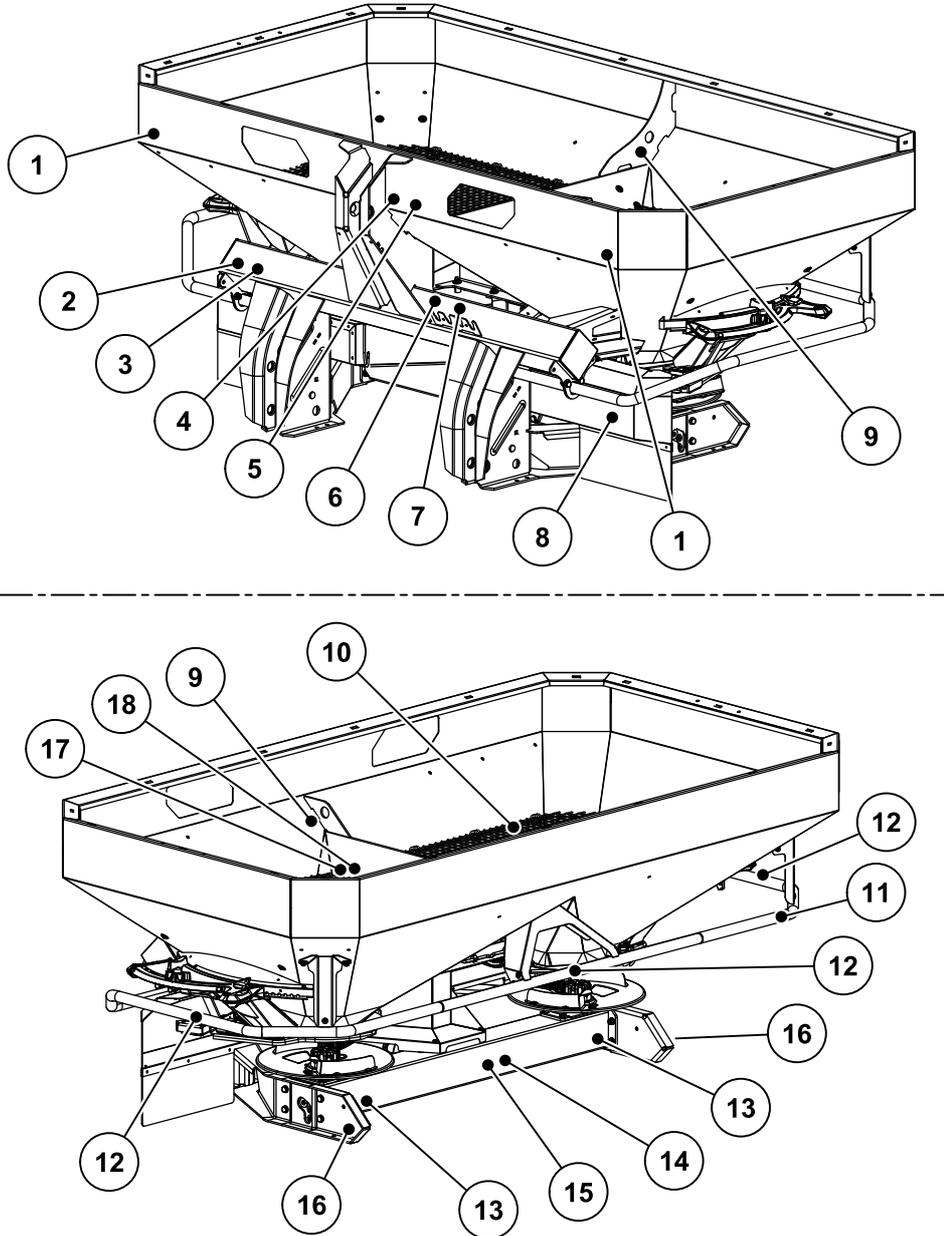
Emplacement des dispositifs de protection, des étiquettes d'avertissement et d'instruction et des réflecteurs
